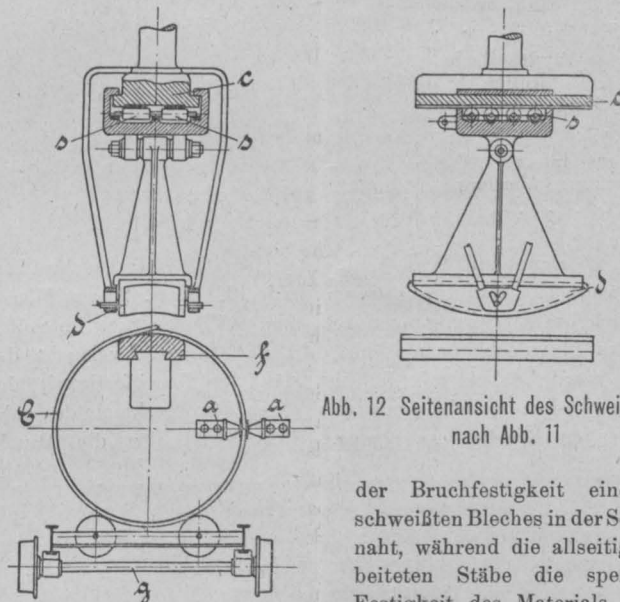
Seitenansicht des Schweißsektors nach Abb. 11
